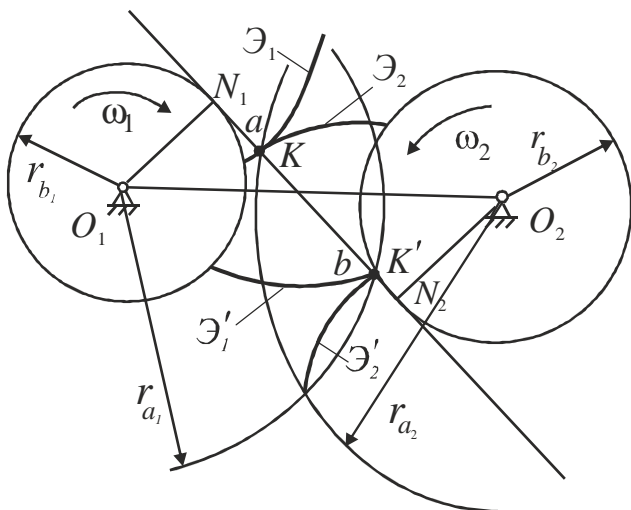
Линия зацепления эвольвентных зубчатых колес
